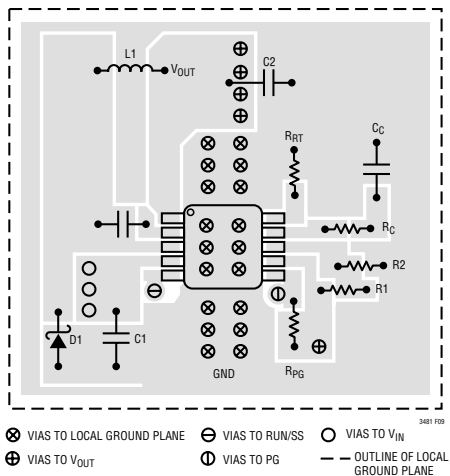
：上佳的 PCB 布局保证了正确的低 EMI 操作
